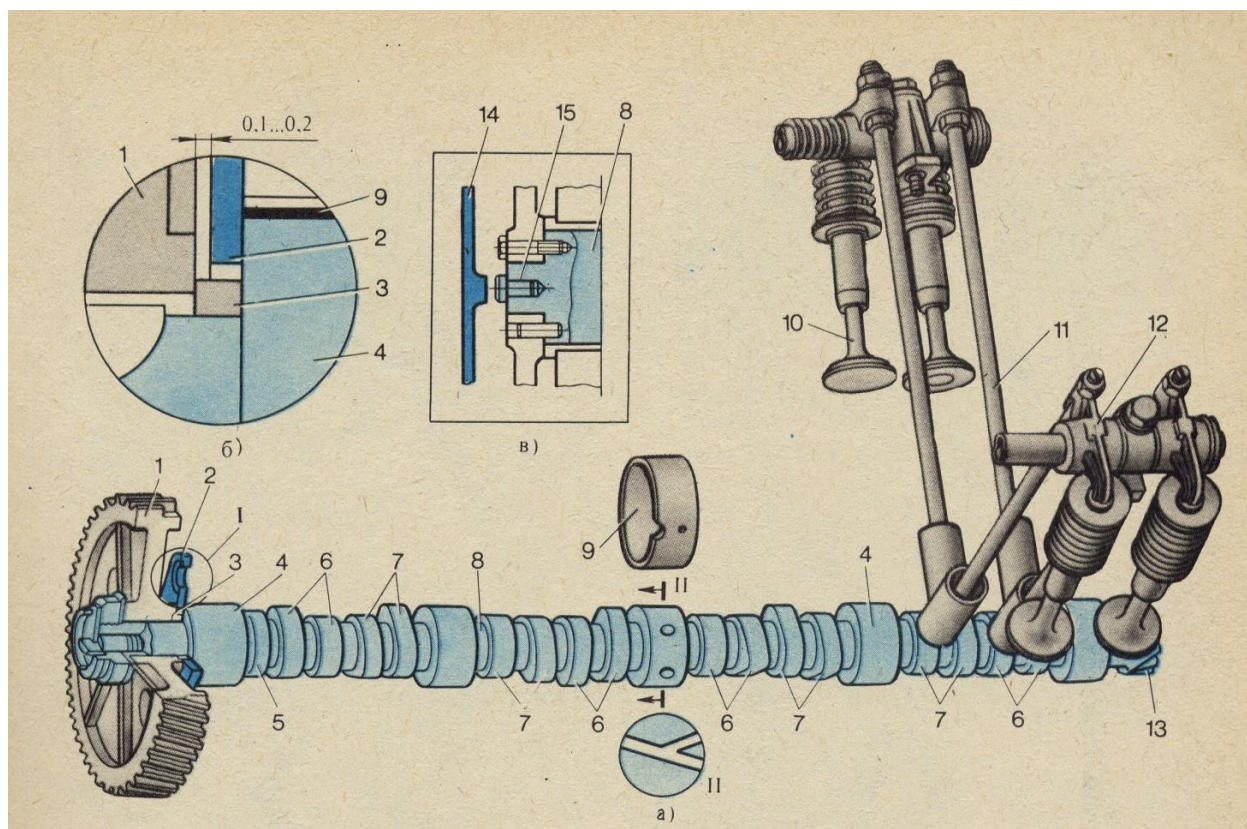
Распределительный механизм V - образного двигателя: а - устройство, б, в - схемы ограничения осевого люфта распределительного вала; 1 - приводная шестерня, 2 - упорный фланец, 3 - распорное кольцо, 4 - опорные шейки, 5 - эксцентрик привода топливного насоса, 6 - кулачки выпускных клапанов, 7 - кулачки впускных клапанов, 8 - распределительный вал, 9 - втулка, 10 - впускной клапан, 11 - штанга, 12 - коромысло, 13 - шестерня привода масляного насоса и прерывателя распределителя, 14 - крышка распределительных шестерен, 15 - подпятник
